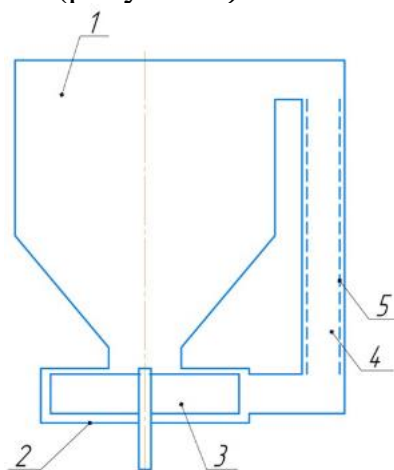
Схема установки для приготовления зерновой патоки с пассивным дезинтегратором в виде цилиндрической решетки: 1 – бак; 2 – корпус насоса; 3 – крыльчатка насоса; 4 – обводной канал; 5 – трубный дезинтегратор
